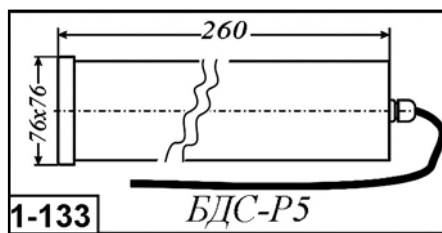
Внешний вид и габаритные размеры блока детектирования БДС-Р5
